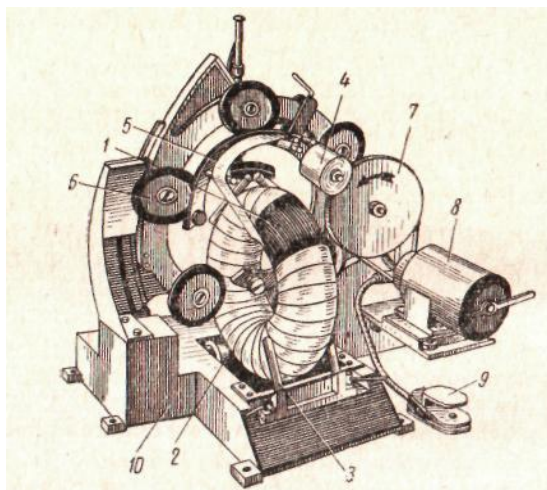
Машина для упаковки дроту: 1 - моток дроту; 2 - приводний опорний ролик; 3 - напрямна; 4 - обплітальний рулон; 5 - кільце; 6 - притискний ролик; 7 - обертає диск; 8 - двигун; 9 - пускова педаль; 10 – станина.
